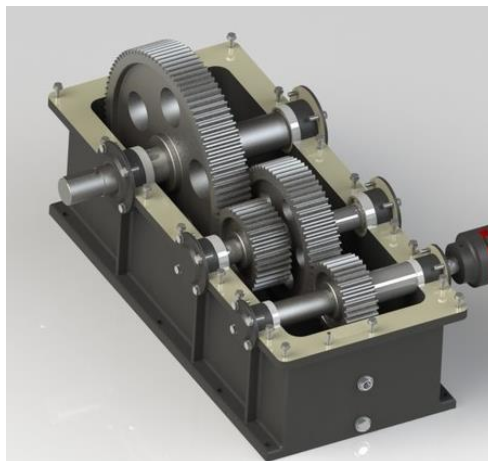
Redutor de engrenagens cilíndricas com dentes helicoidais
